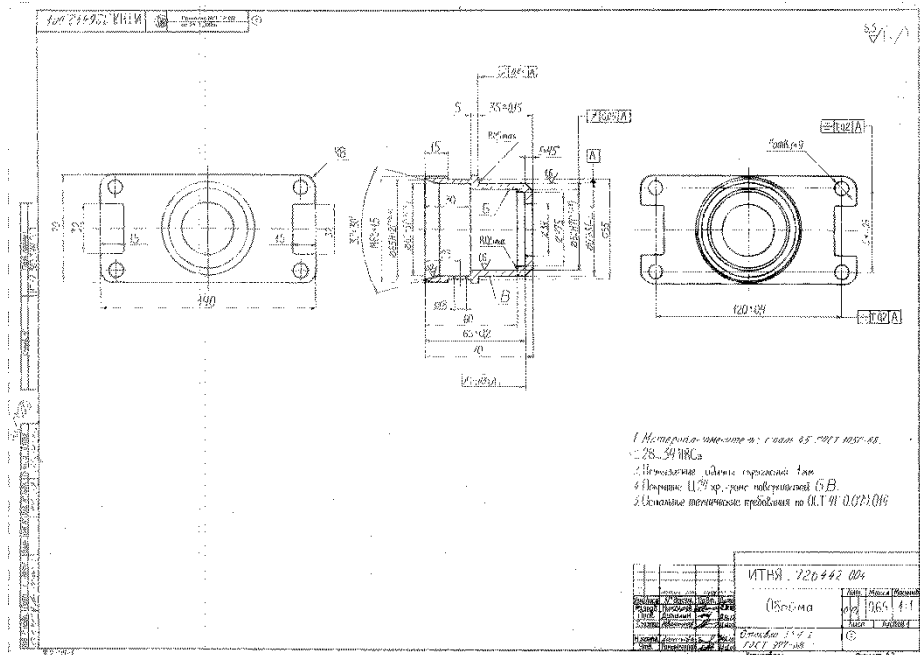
Чертеж детали ИТНЯ.726442.004
